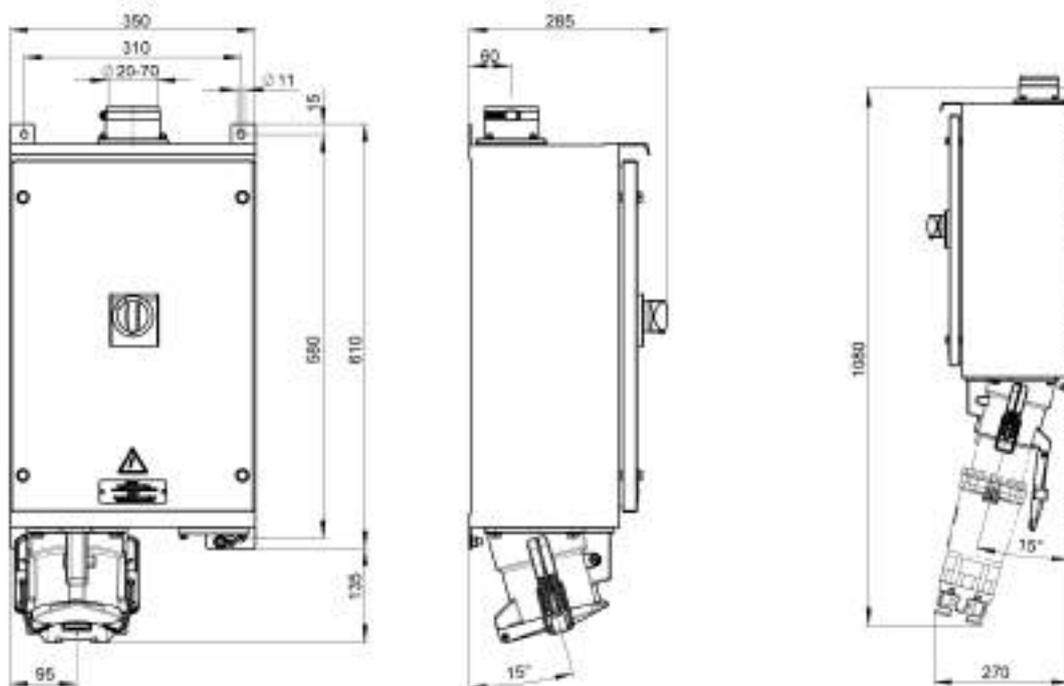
Abmessungen Anschlusskasten mit Leistungsschalter CUCB D-Line, C-Line (160A – 250 A) in mm
